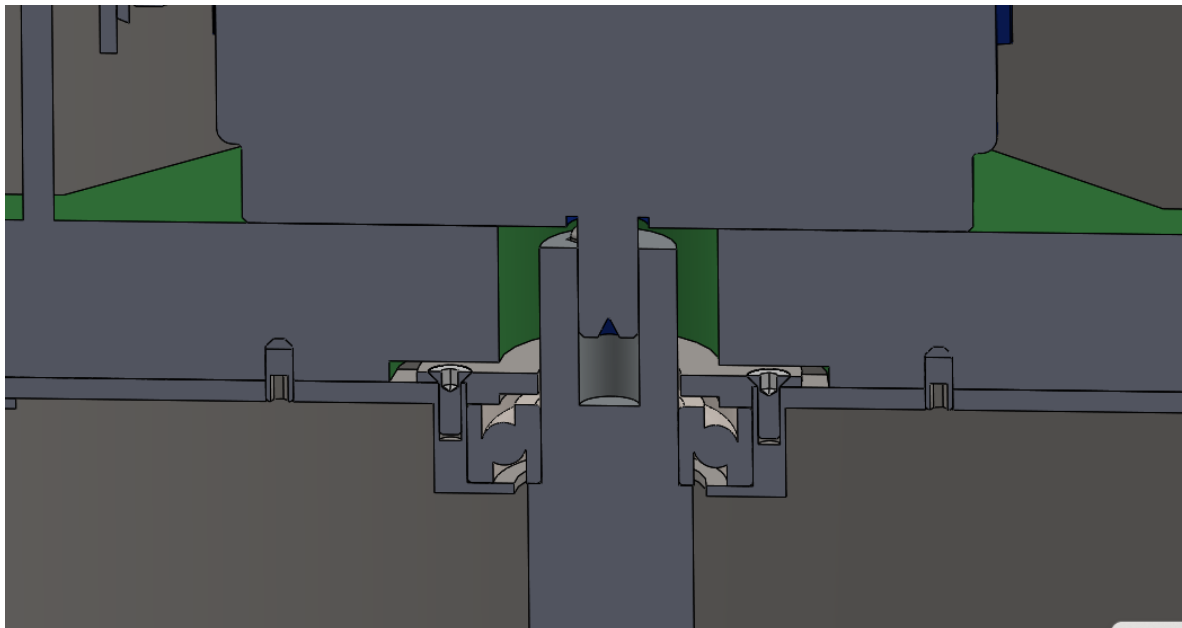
Зовнішній вигляд радіально упорного підшипника та захисної пластини, розташованого біля шпонкового з'єднання вала двигуна зі шнеком.
